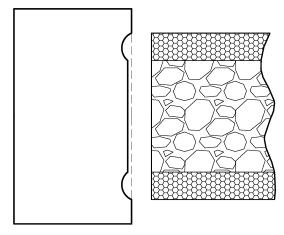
Схема износа резца при фрезеровании ламинированных ДСтП
